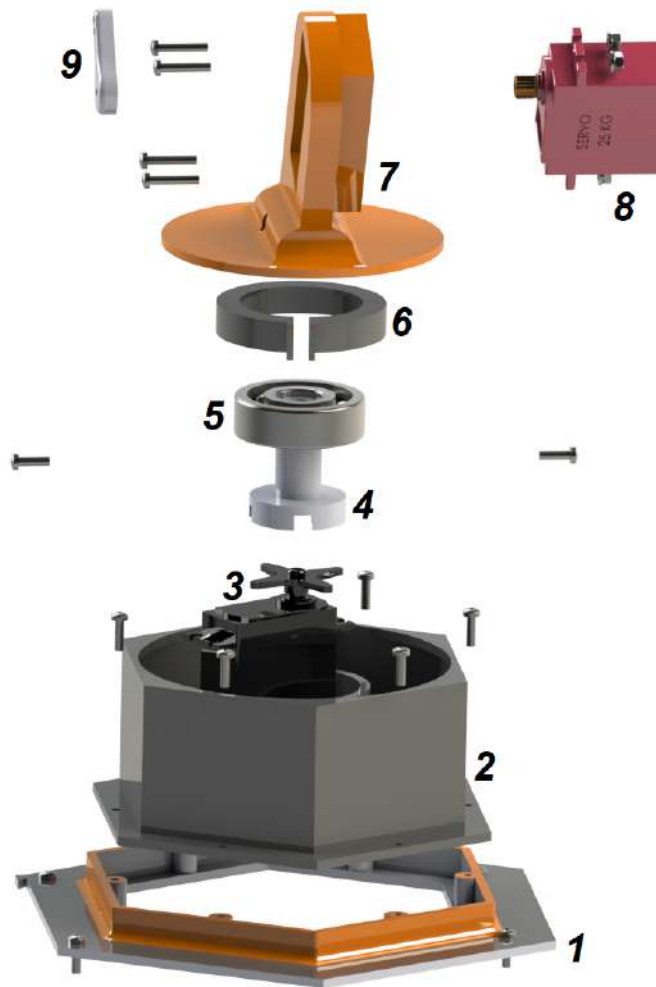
CAD de vista explosionada para ensamble del 1.er gdl. Fuente: Elaboración propia
